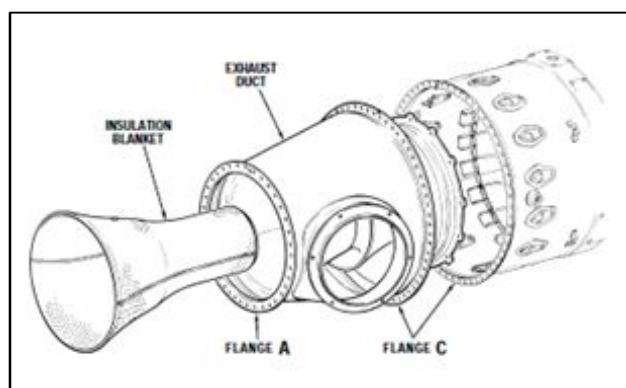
Componentes del ducto de escape del motor PT6A-25
